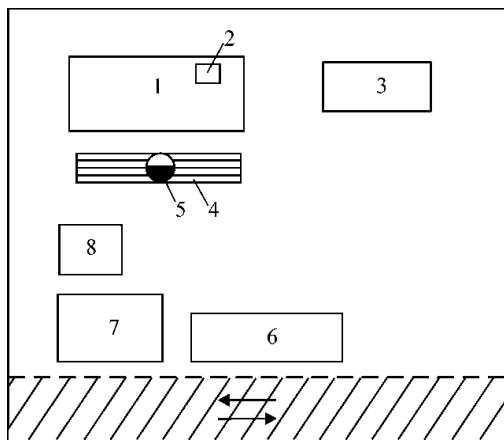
Робоче місце електрозварника ручного зварювання (площа 10 м²): 1 – стіл для електрозварювальних робіт; 2 – напівавтомат зварюваний; 3 – перетворювач зварювальний; 4 – килим діелектричний; 5 – стілець; 6 – стелаж для деталей пересувної; 7 – шафа для інструменту; 8 – ящик для піску.
